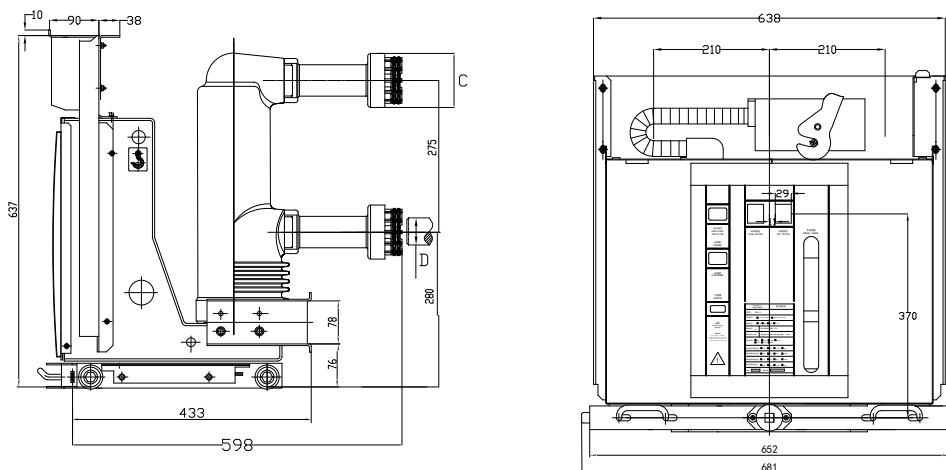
移开式 VPN-800 型柜型外形尺寸图
